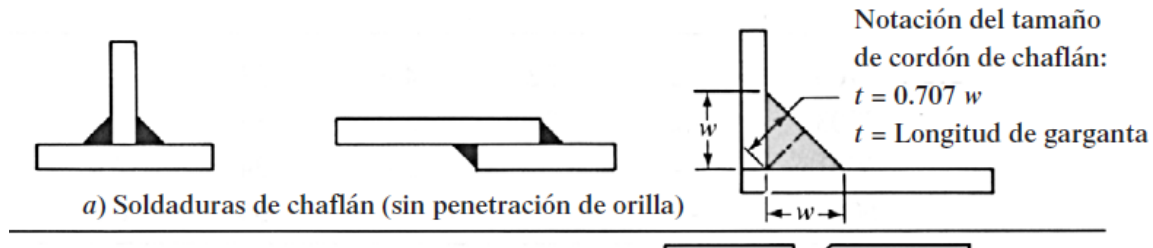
ilustracion de union por soldaduras de tipo chaflan [20].
